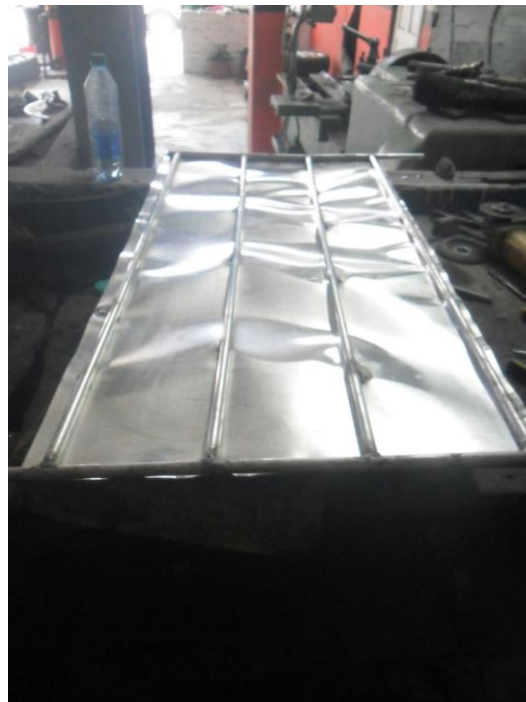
Soldadura final de serpentín y placas
